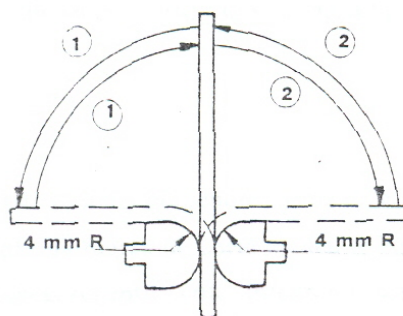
ENSAYO DE DOBLADO DE PROBETAS EN FORMA DE PLACA
